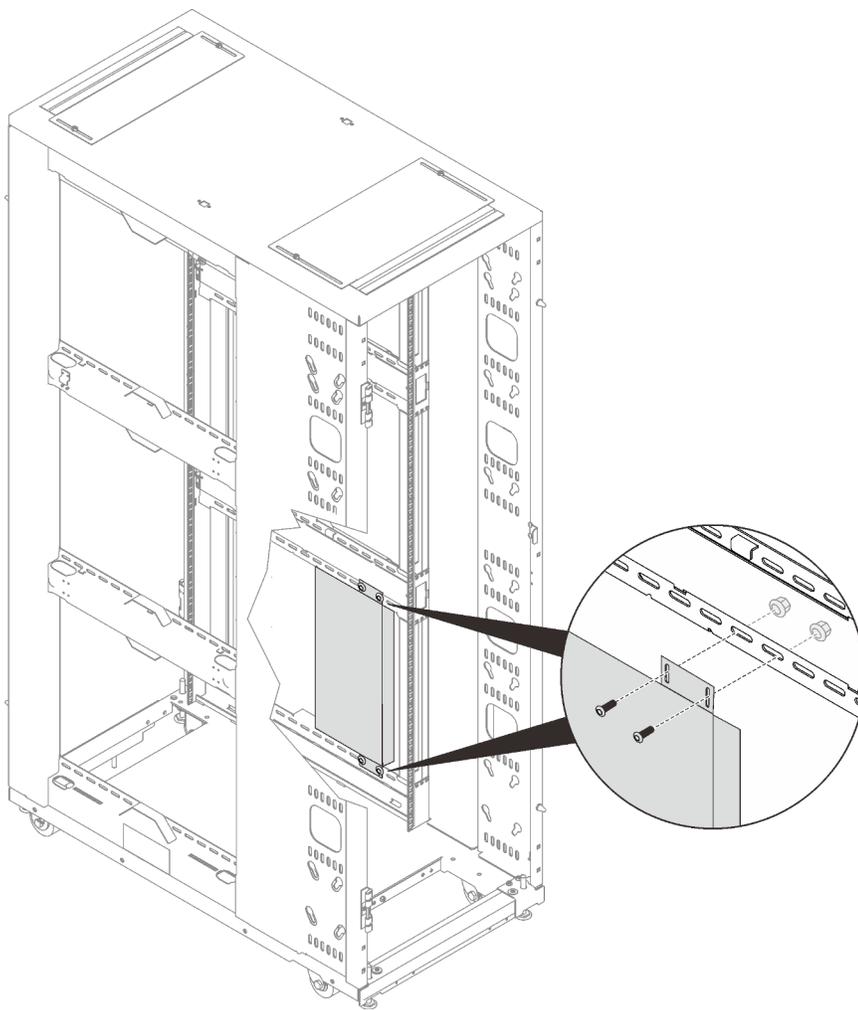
Installazione di un dispositivo 1U nella parte laterale del rack
